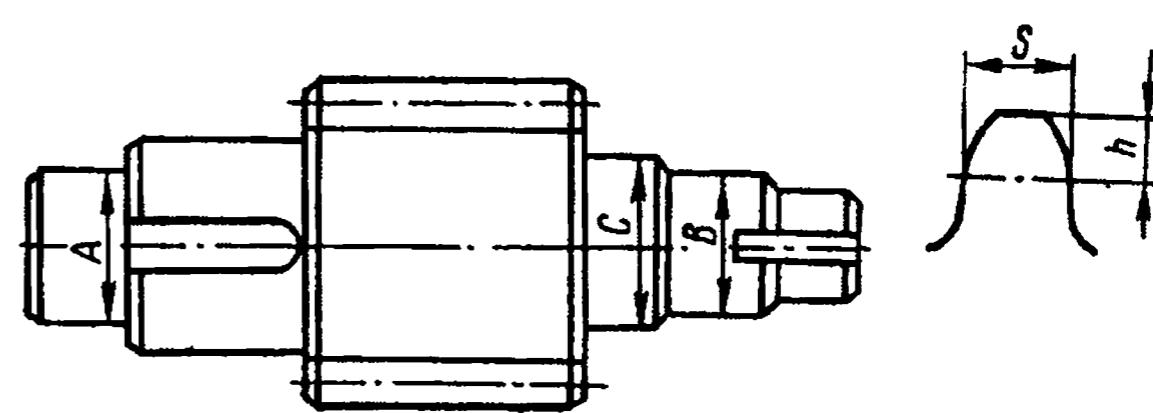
Колесо зубчатое ведущее цилиндрическое
